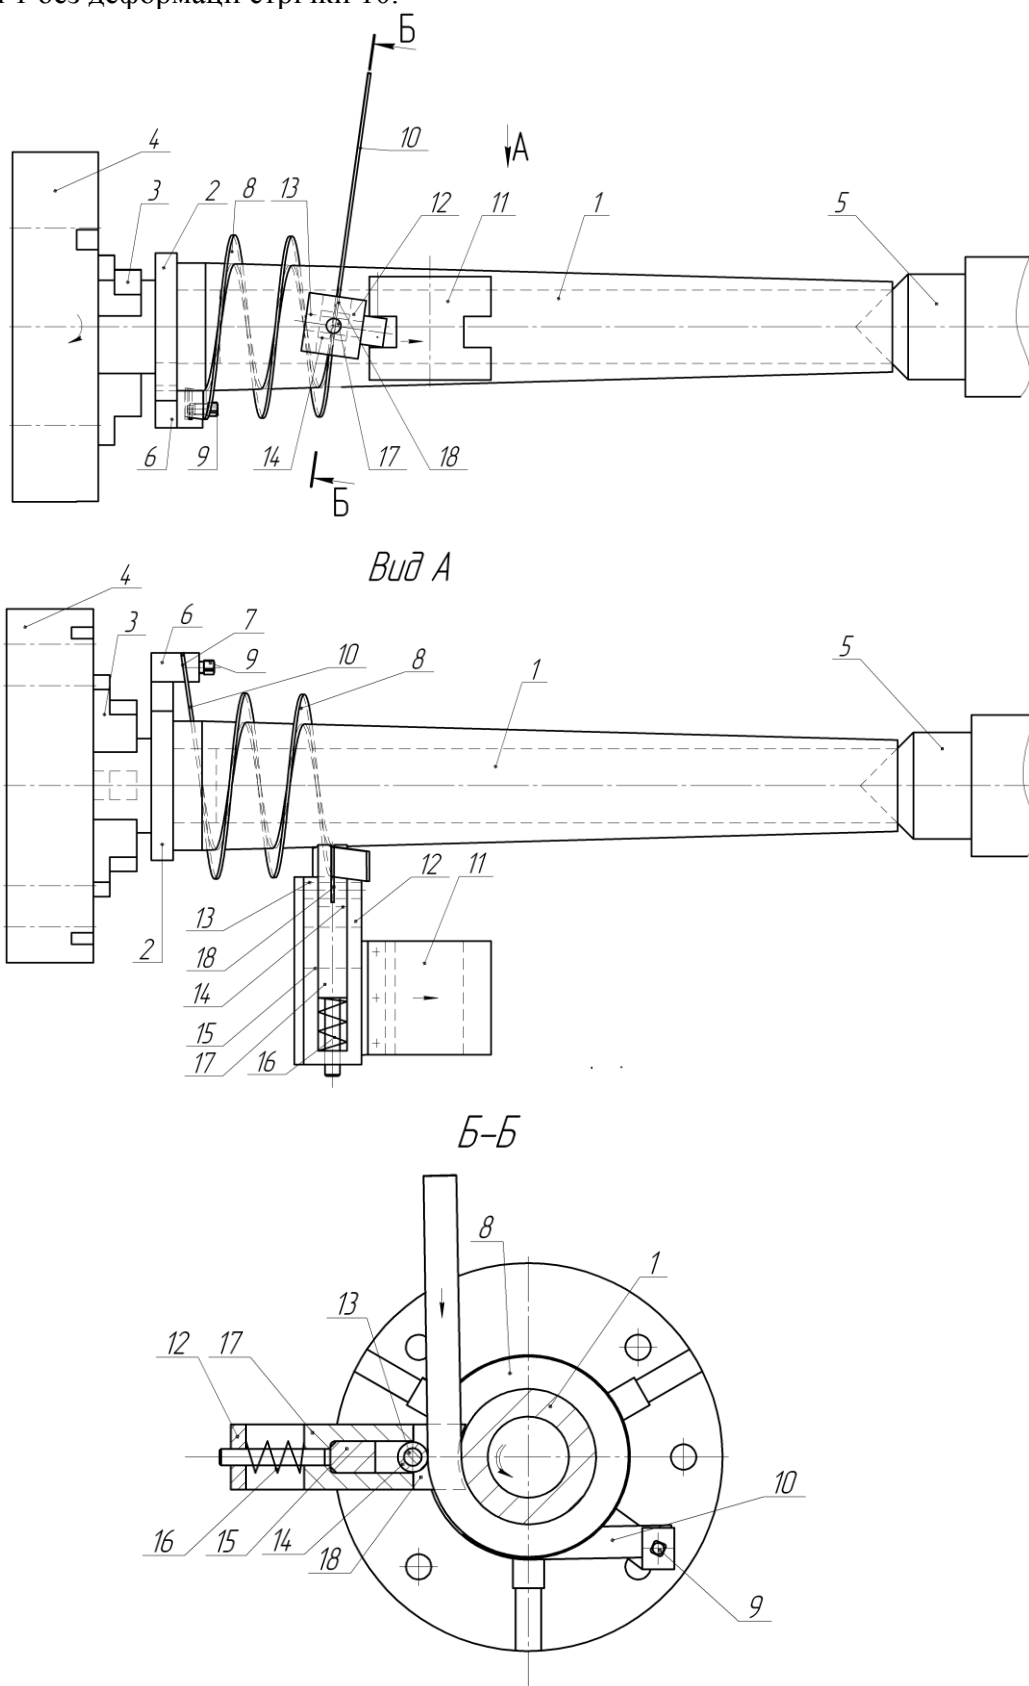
Конструкція пристрою для виготовлення навивних стрічкових гвинтових заготовок
